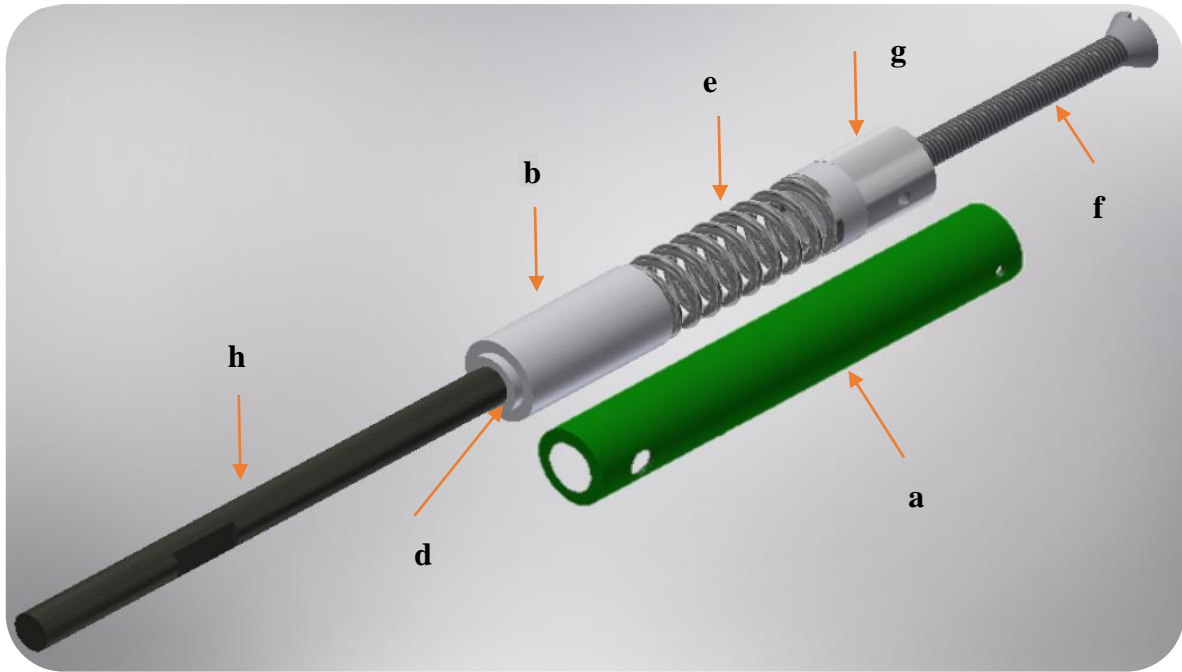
Vista isométrica del módulo de amortiguación y partes que lo componen.
